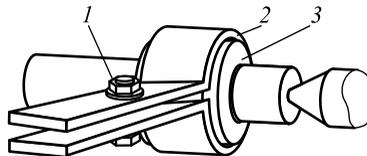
Схема ручной притирки цилиндрической поверхности
